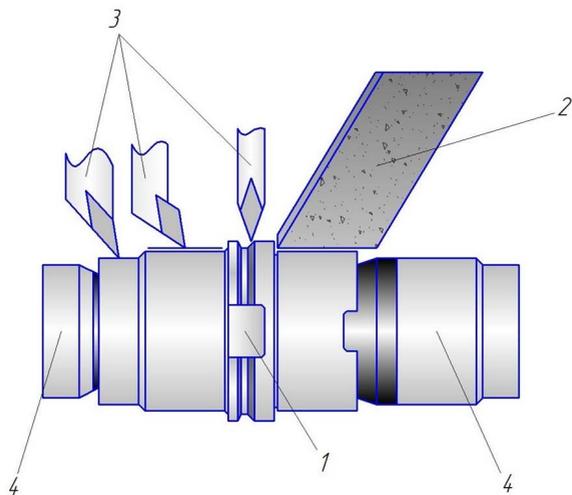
Схема комбинированной обработки цилиндрических поверхностей резцами и шлифовальным кругом: 1 – заготовка; 2 – круг; 3 – резцы; 4 – центры
